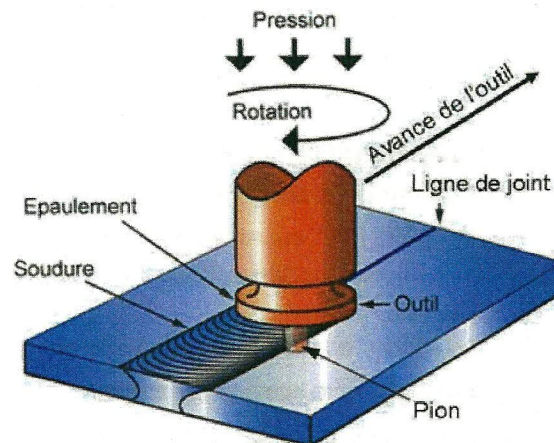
schéma du procédé de soudage par friction malaxage (extrait de CES EduPack).
